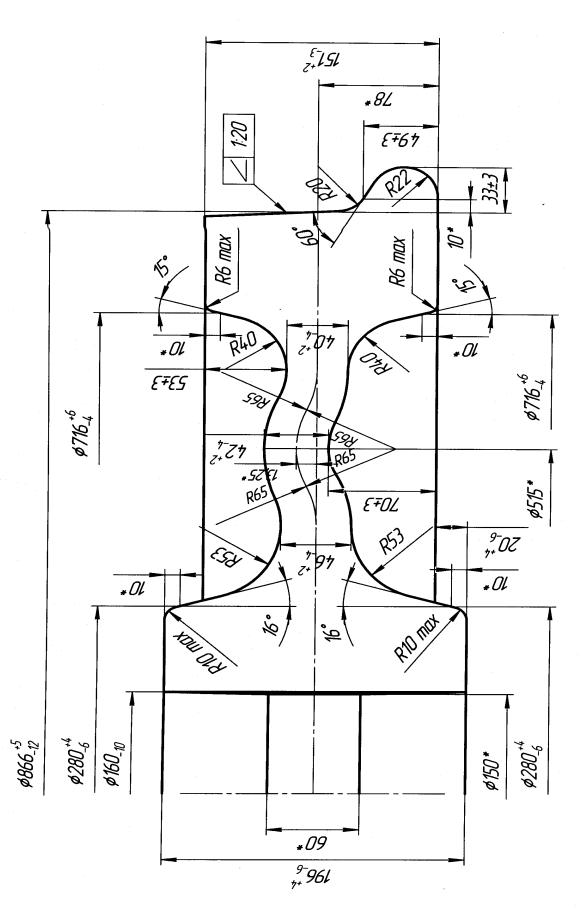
Колесо черновое Ø 866 мм под чистовое Ø 840 мм черт. № КР-0028-09 изм.3 для Великобритании. Масса чернового колеса, рассчитанная на  $^2/_3$  поля допуска = 461кг.
